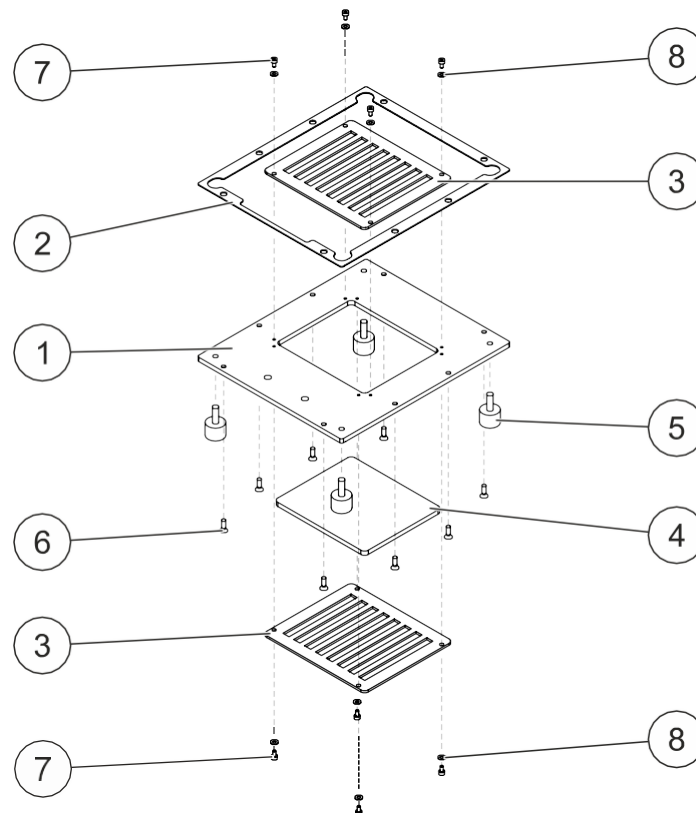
Baugruppe Grundplatte PQ15E-HT
